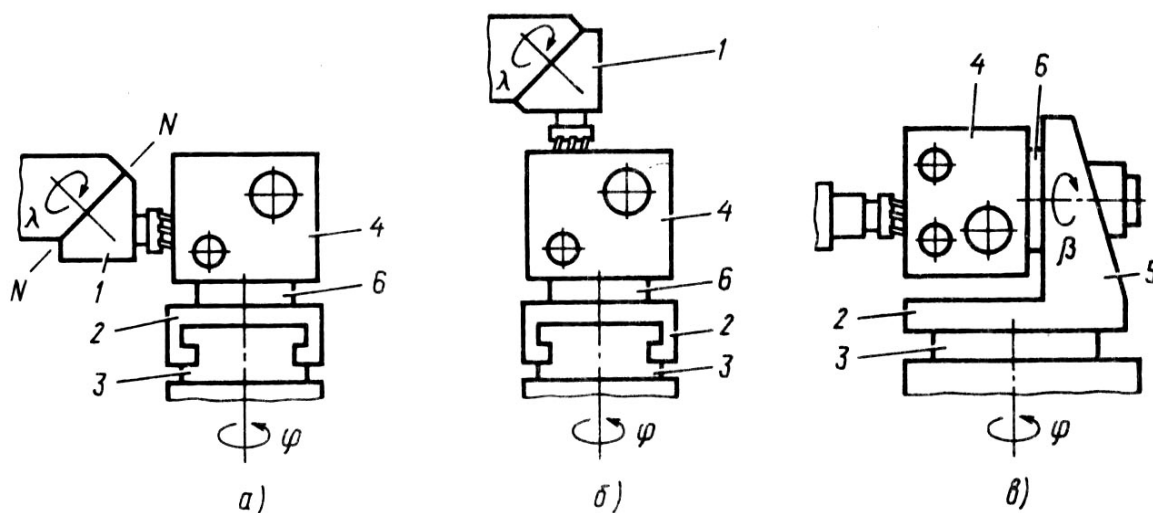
Обработка заготовки на спутнике с пяти сторон: а, б – с использованием поворотной головки для инструмента, установленного на шпинделе станка; в – с использованием поворотного приспособления для заготовки на спутнике; 1 – поворотная головка для инструментов; 2 – спутник; 3 – поворотный стол станка; 4 – заготовка; 5 – приспособление на спутнике для поворота заготовки; 6 – подкладная плита
